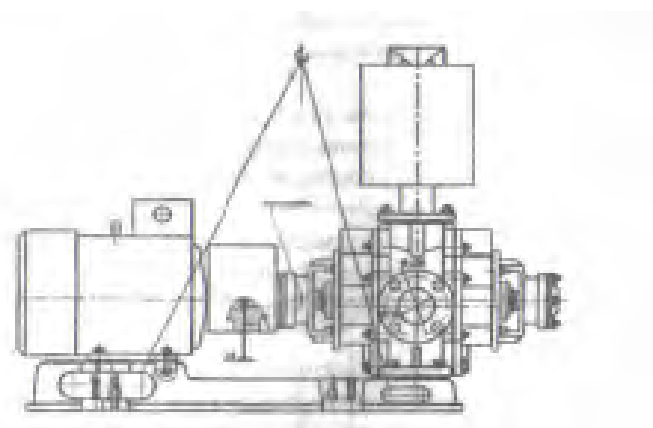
Схема строповки при транспортировании электроагрегата
